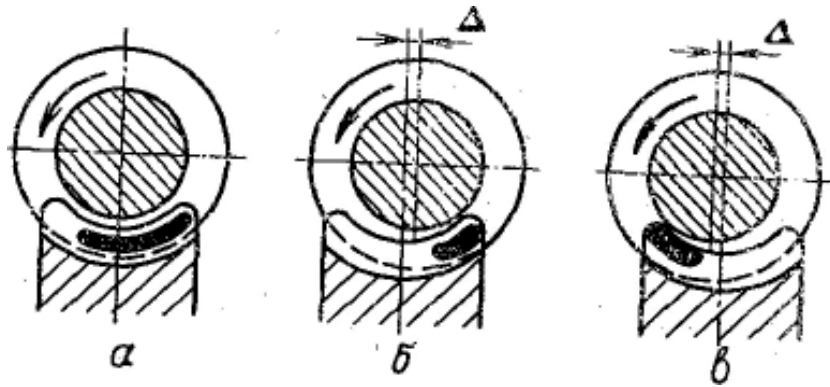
Перевірка установки черв'яка щодо черв'ячного колеса
